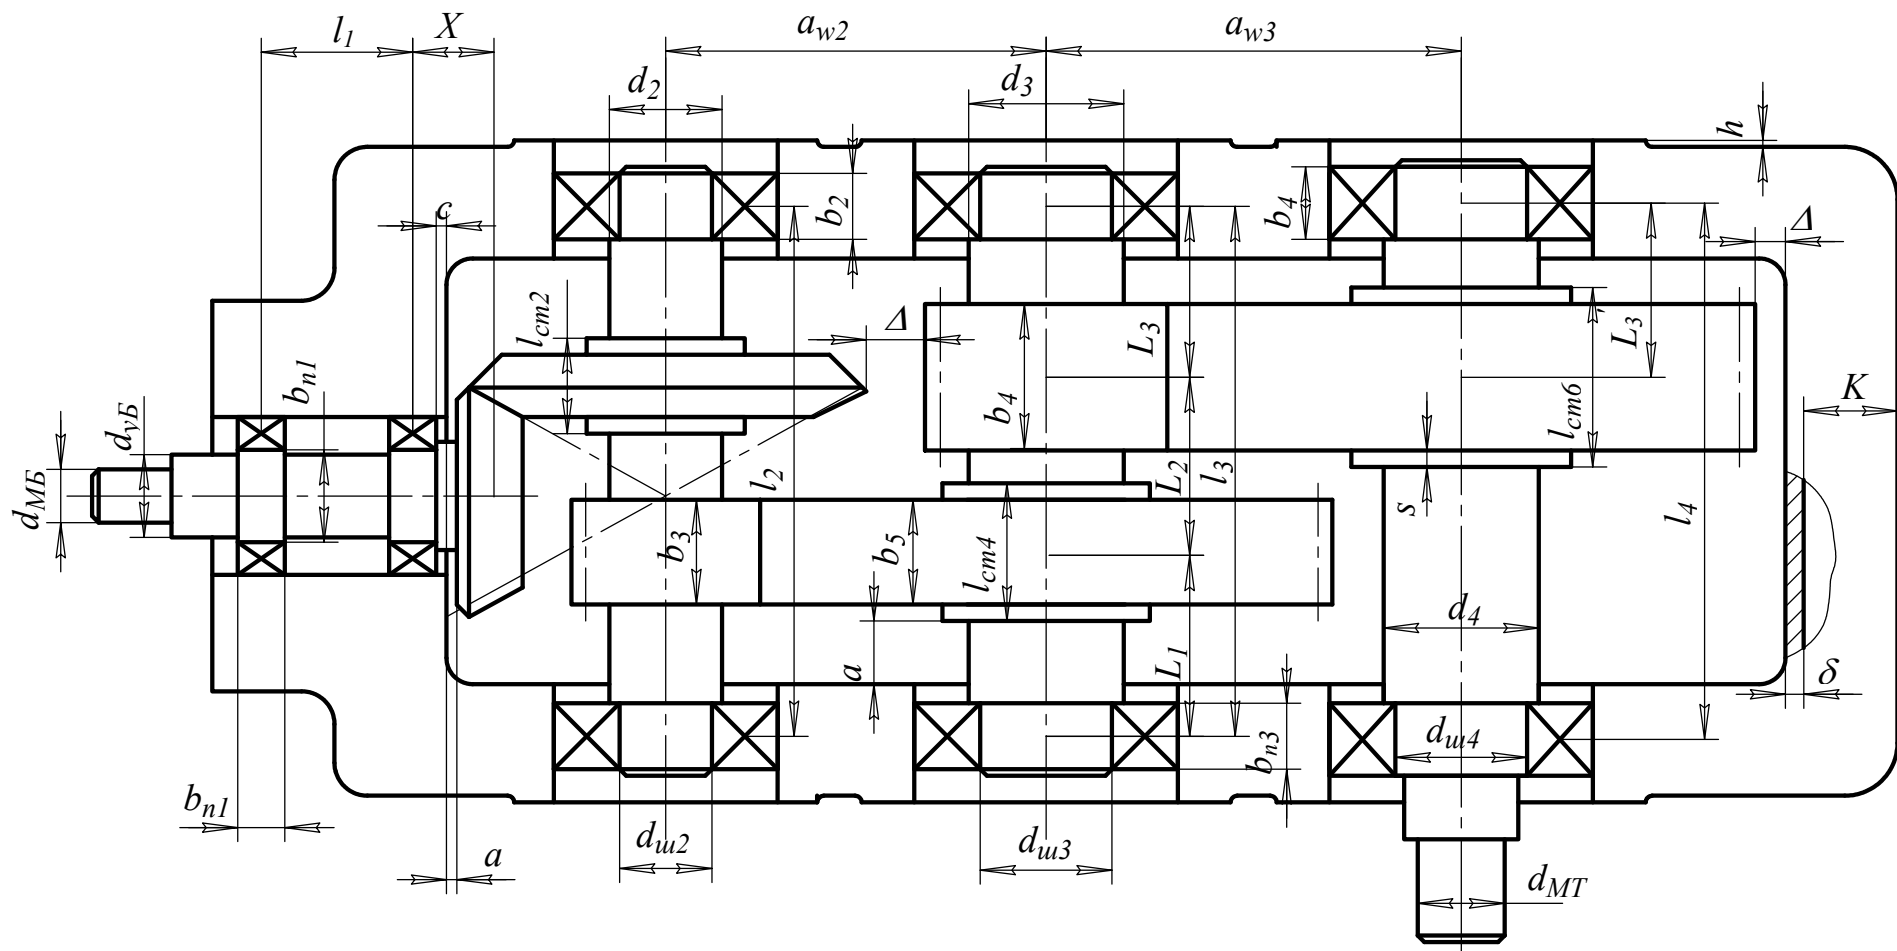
Ескізне компонування триступеневого конічно-циліндричного редуктора
